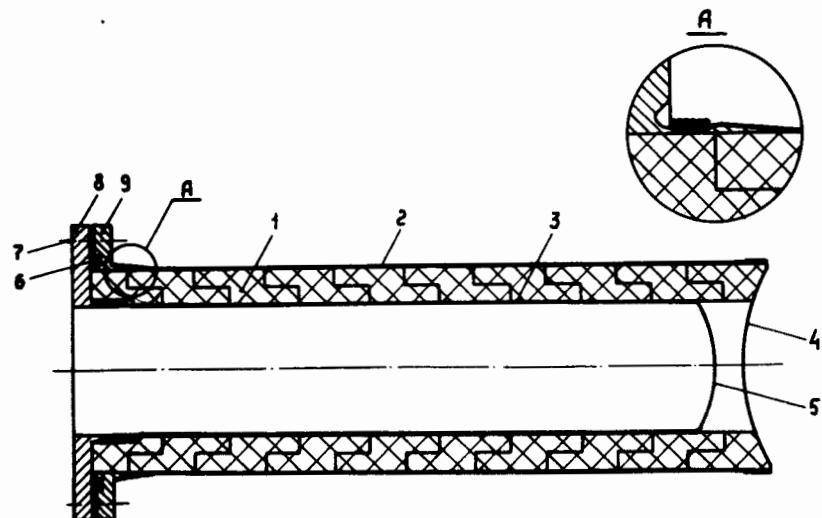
Схема конструкции кожуха из пенопласта и лавсана: 1 - цилиндр из пенопластовых колец; 2 и 3 - обечайки из лавсановой пленки; 4 и 5 - донышки из лавсановой пленки; 6 - прокладка; 7 - шпилька; 8 и 9 - фланцы.
